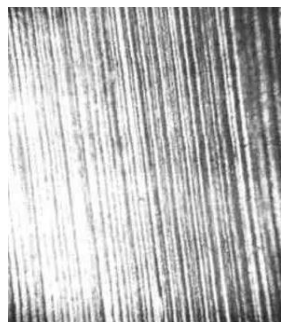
Внешний вид поверхности изношенного плунжера (x80)
